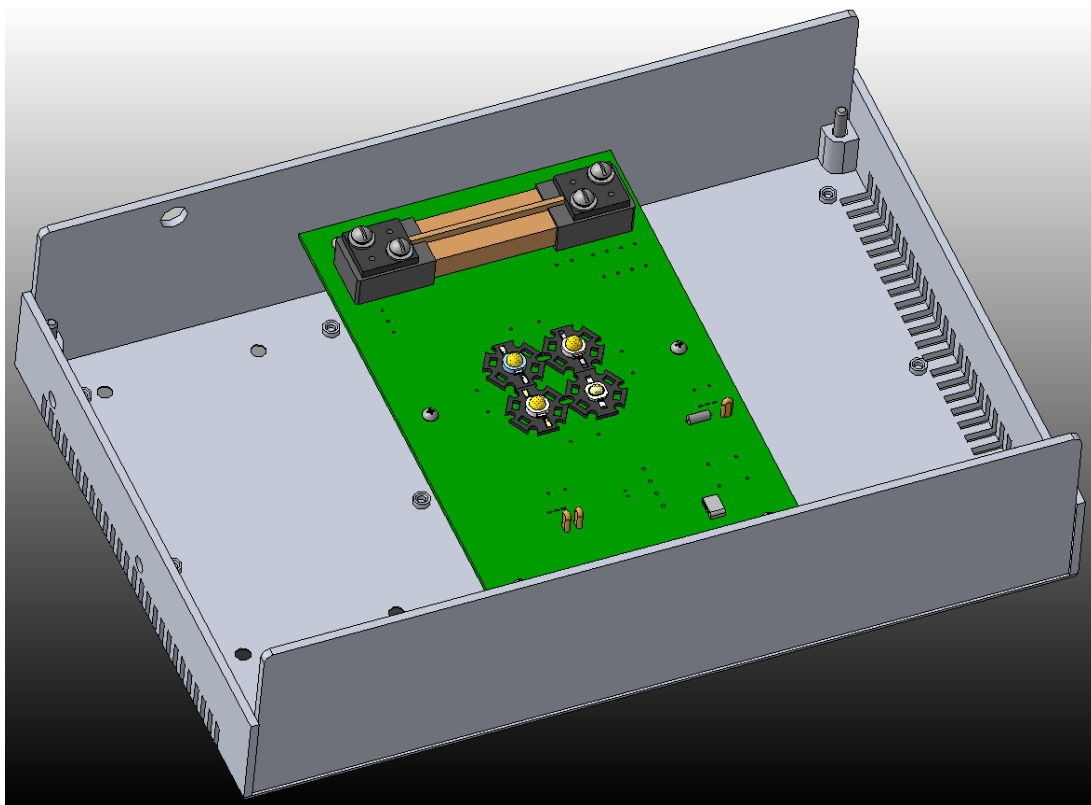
Расположение в корпусе платы и элементов на ней
